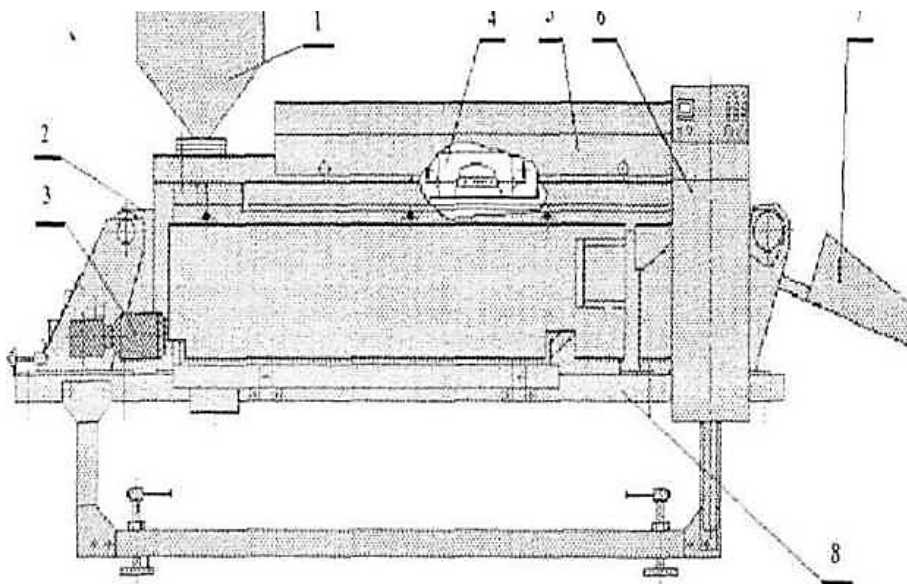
Загальний вид установки для термообробки зернової Зсировини
